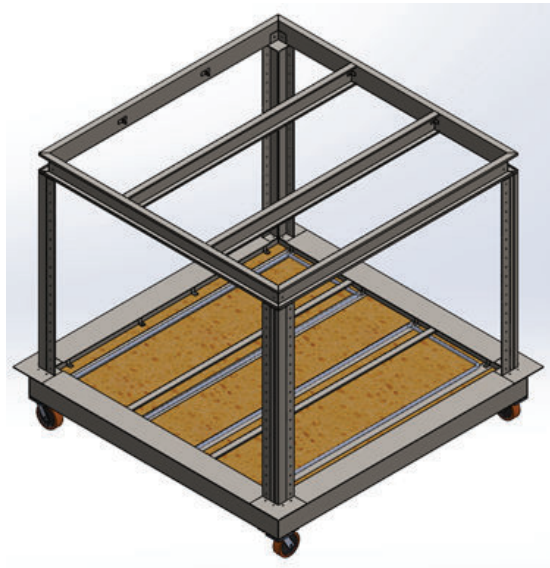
Colocación de las vigas del techo (Fuente propia)
